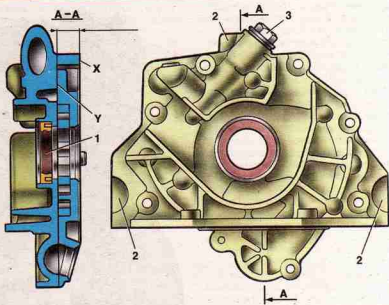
Точки крепления крышки масляного насоса при фрезеровании плоскостей: 1 – сальник коленчатого вала; 2 – точки крепления крышки; 3 – пробка редукционного клапана; X, Y – плоскости фрезерования
